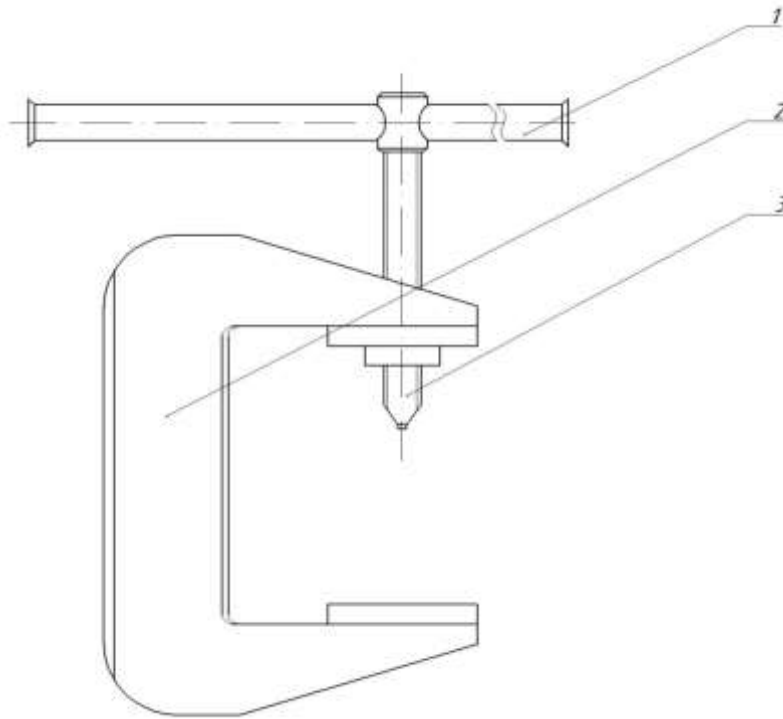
Знімач хрестовин карданних валів СВК1: 1 – ручка; 2 – корпус; 3 – гвинт натискний
